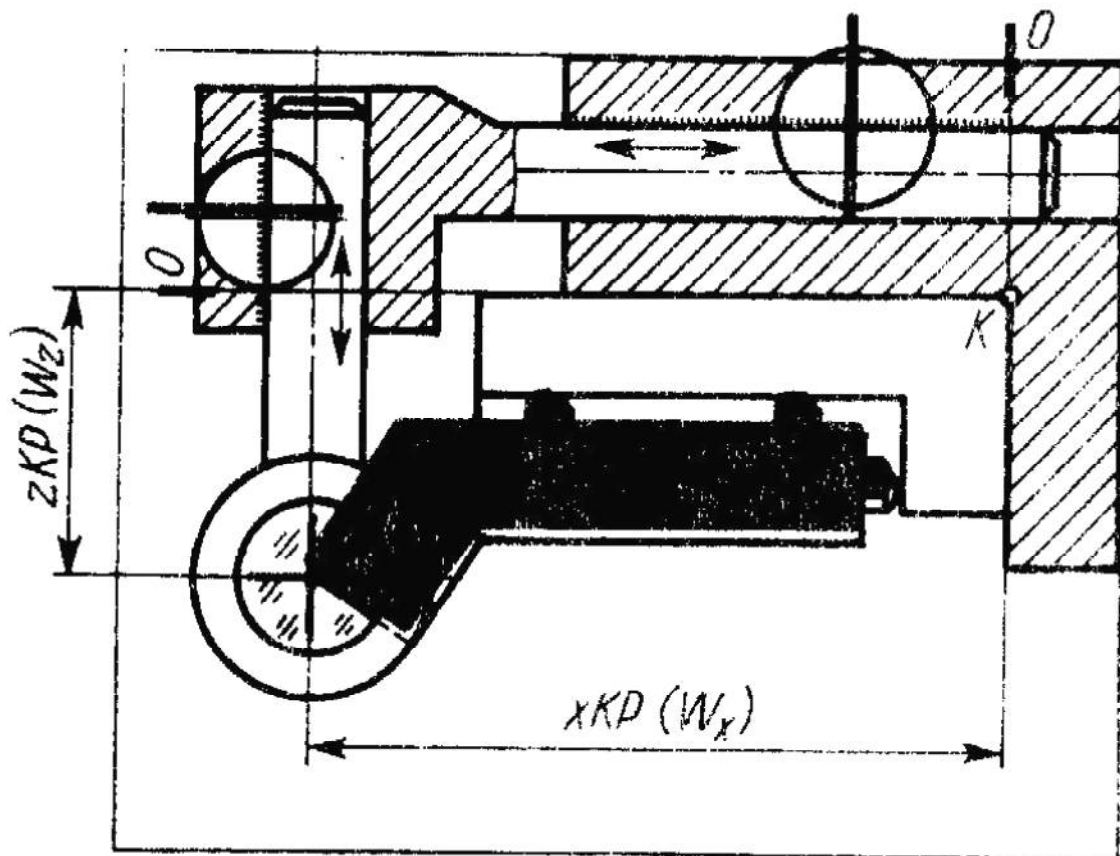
Схема пристрою для налагодження інструмента поза верстатом
